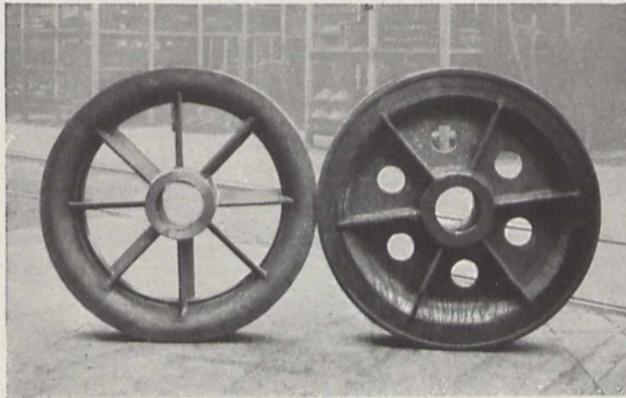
Eine geschweißte und eine gegossene Seilrolle mit gleichem Durchmesser. Die gegossene Rolle wiegt 465 kg, die geschweißte 227 kg
